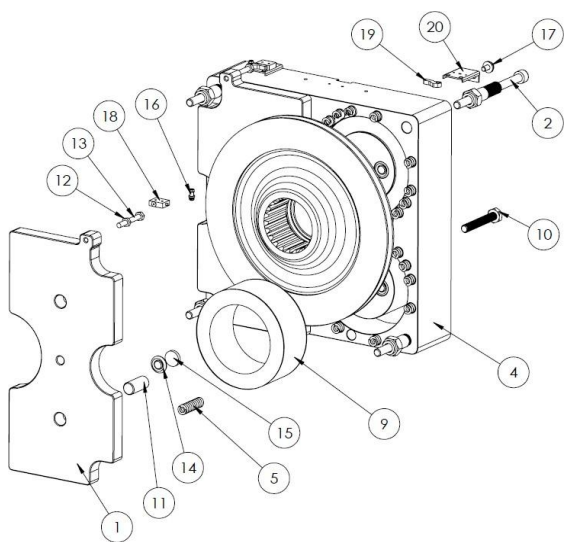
Vista en despiece del conjunto de bobinas de frenos AEMF3-4-9-10
